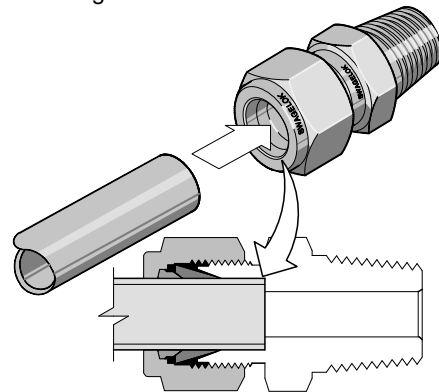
Asegúrese que el tubo está apoyado firmemente sobre el hombro de la herramienta de pre-ensamblaje
